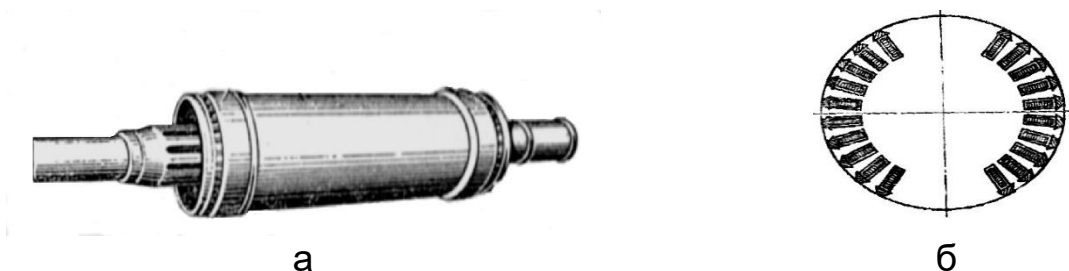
Загальний вигляд ротора турбогенератора –а та поперечний розріз ротора –б
